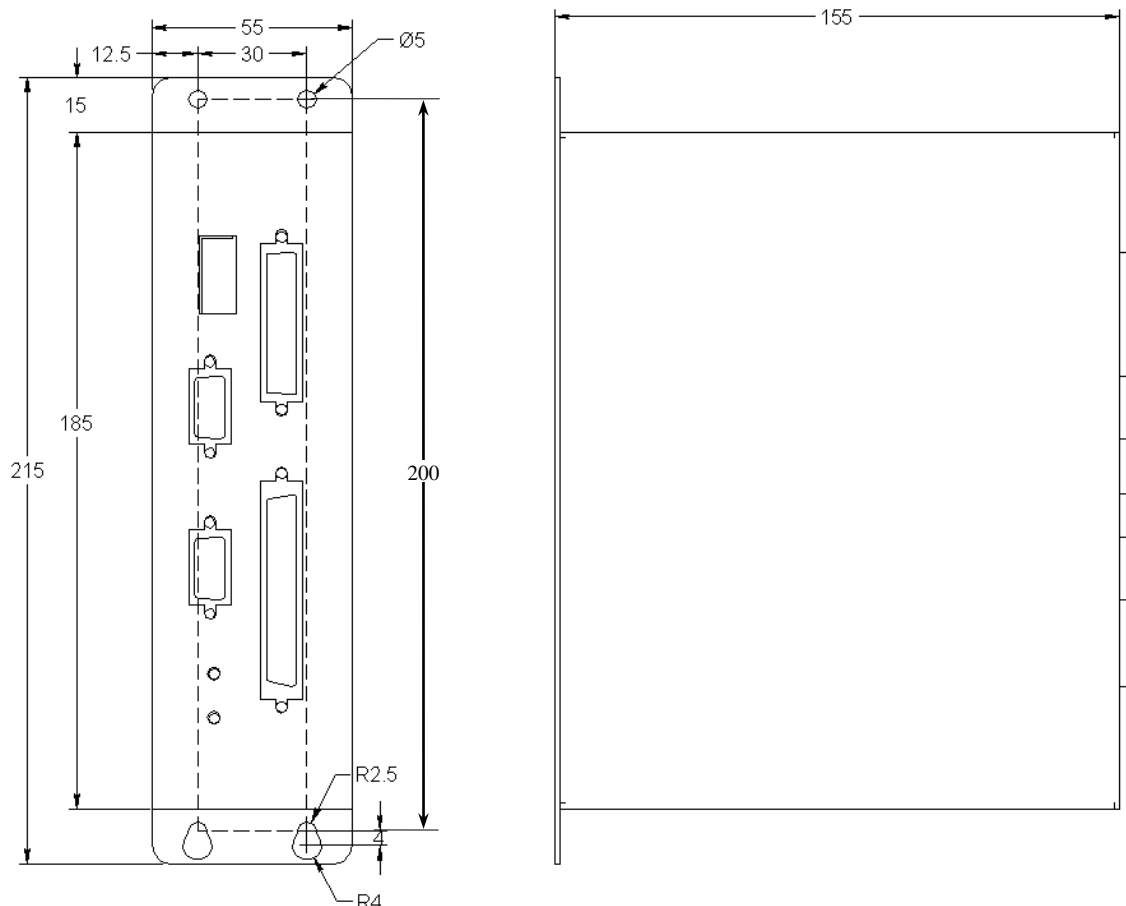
Габаритные и установочные размеры MP SSB I/O NC301-4
